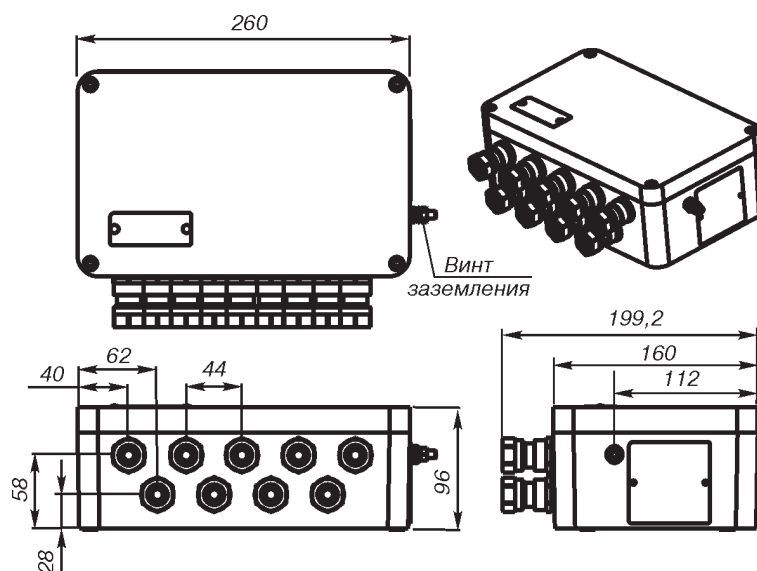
Дополнительная соединительная коробка из алюминия/пластика (монтажный ввод с кабельным уплотнением, код опций JA2 и JP2).
